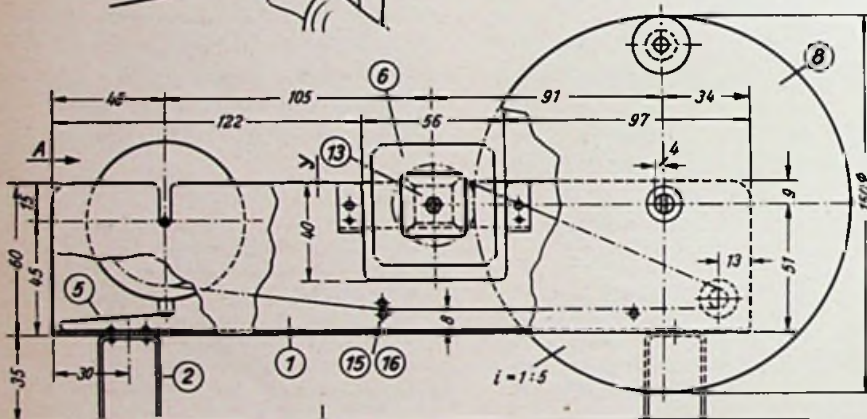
Maßzeichnung einer leicht zu bauenden einfachen Wickelvorrichtung
